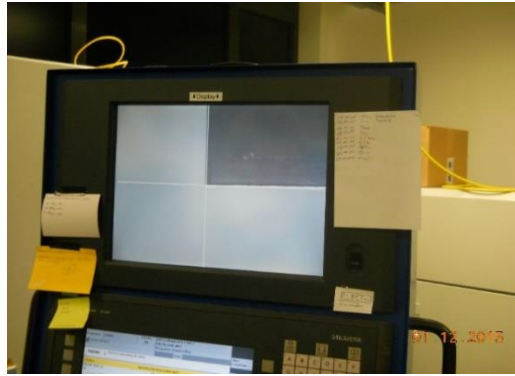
'de Laser kaynak dikişli numunelerin hazırlandığı RUHR Üniversitesi, Laser Kaynak laboratuvarı, Laser kaynak makinası, bilgisayar destekli üç boyutlu hareketli kaynak tezgâhı ile görülmektedir. Kaynak Makinası Pulsalı Nd:YAG-Laser: LASAG SLS 200 CL16, 1064 nm
